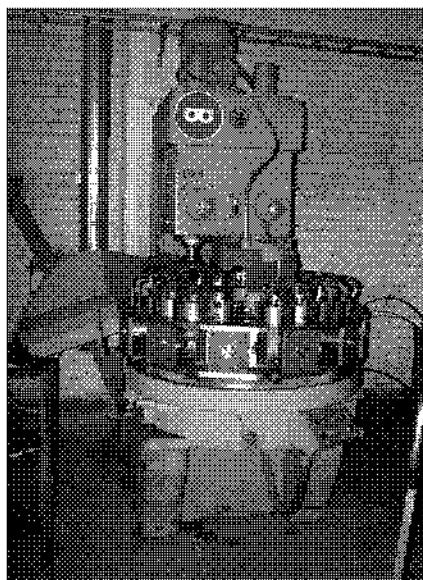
Карусельно-фрезерный станок ЛГ22
